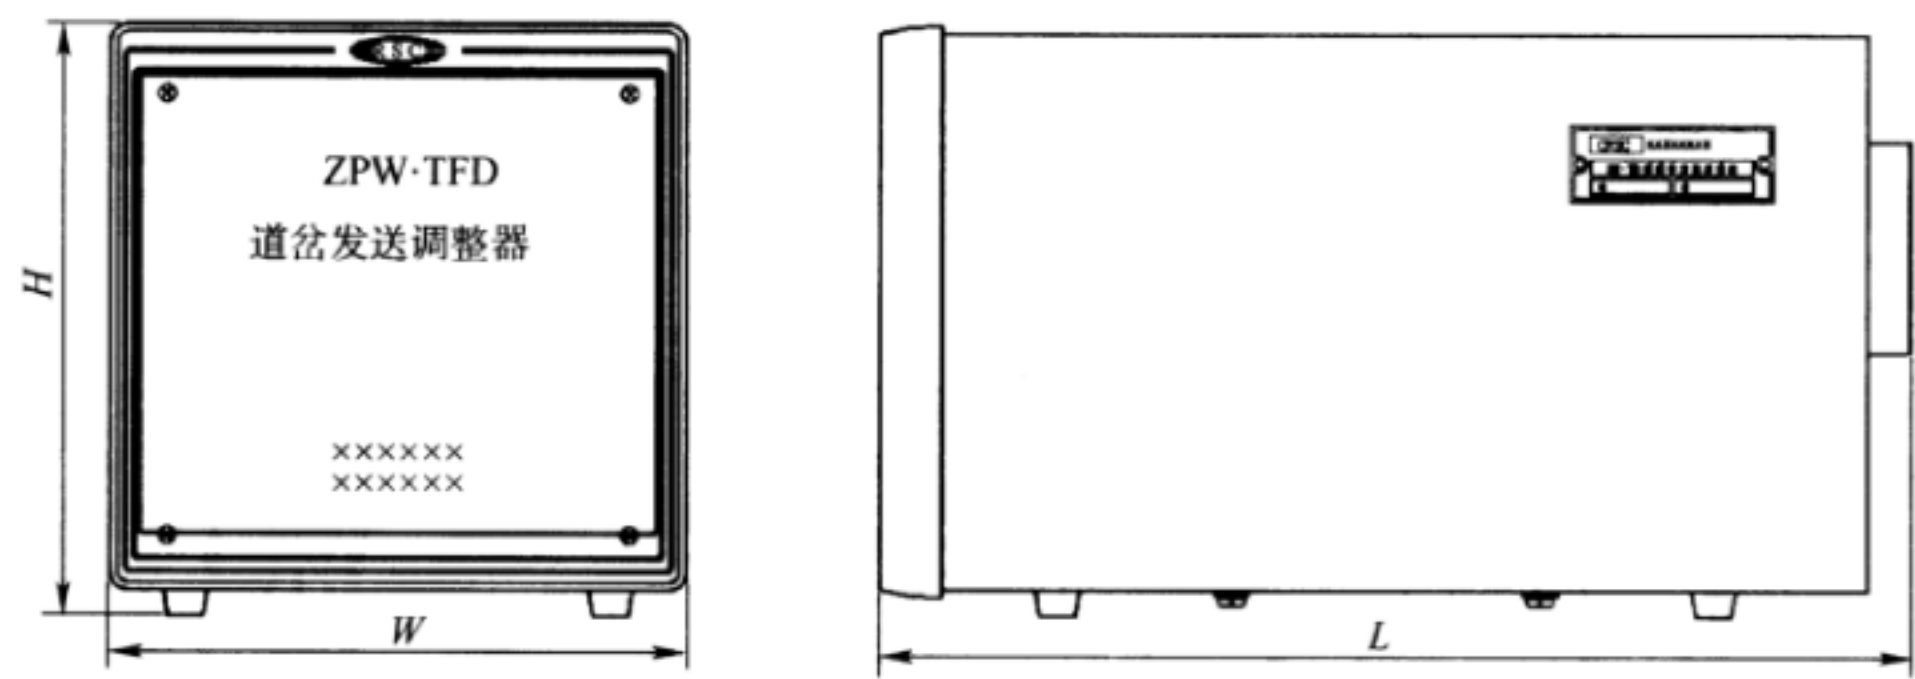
ZPW·TFD 型道岔发送调整器外形尺寸
